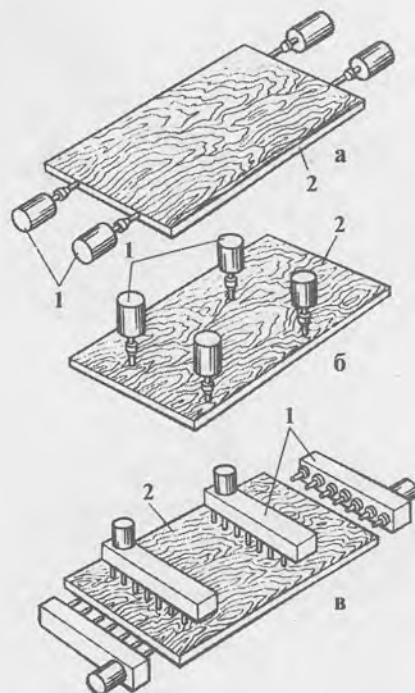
Схемы сверления круглых отверстий на сверлильно-присадочных станках:
